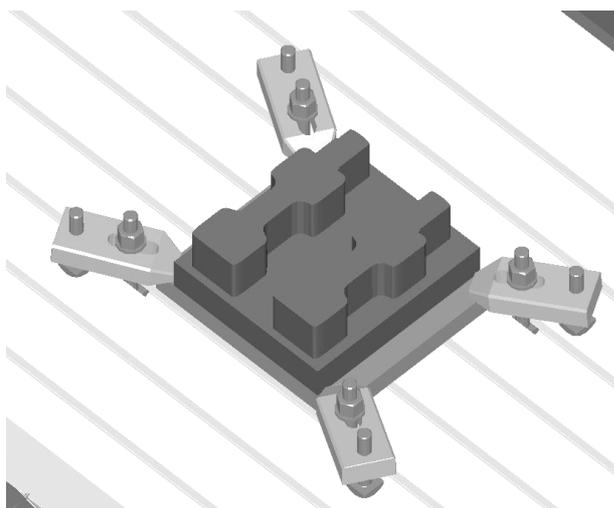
Аналитический эталон геометрии заготовки для чистовой обработки
